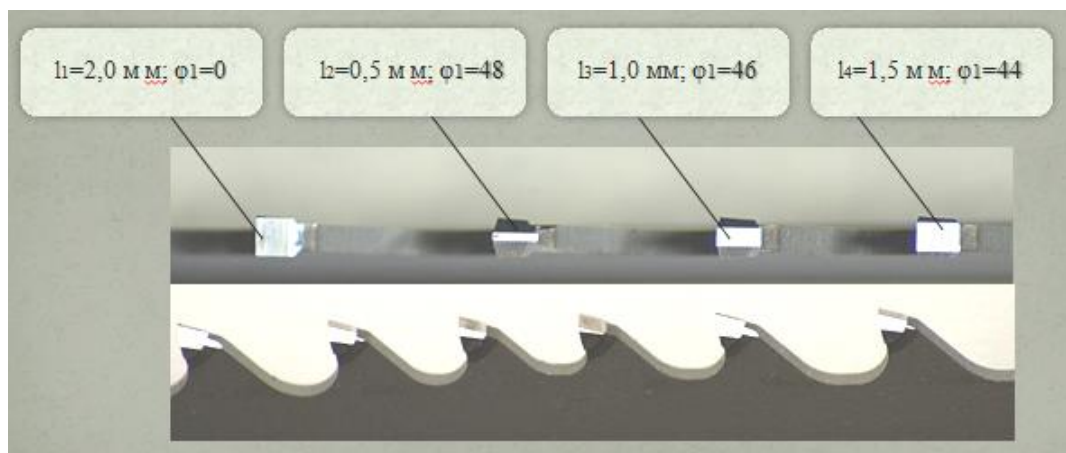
Заточка режущих лезвий пилы при групповой схеме резания
